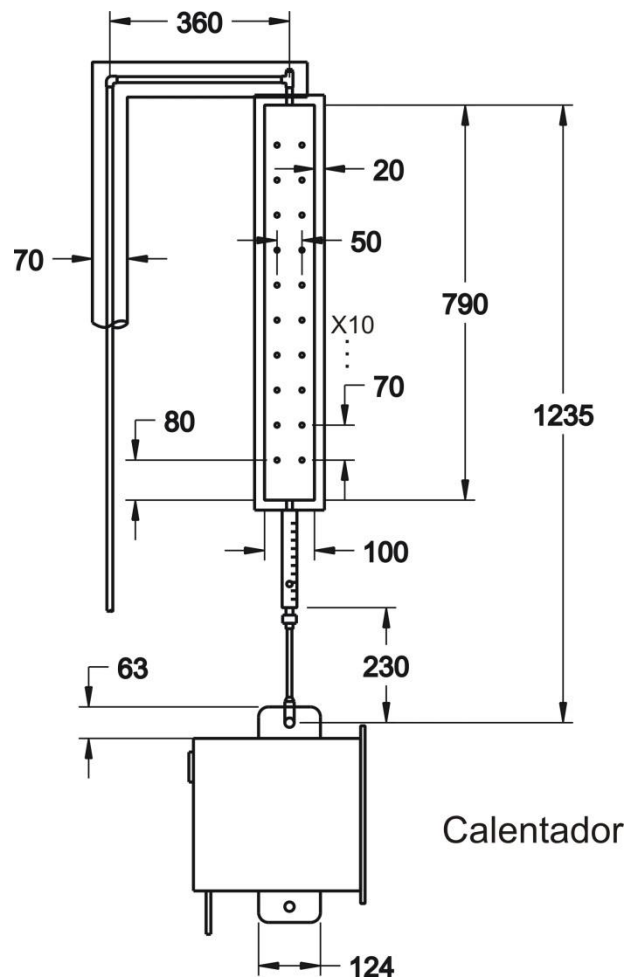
Dimensiones del calentador. Acotaciones en mm.
